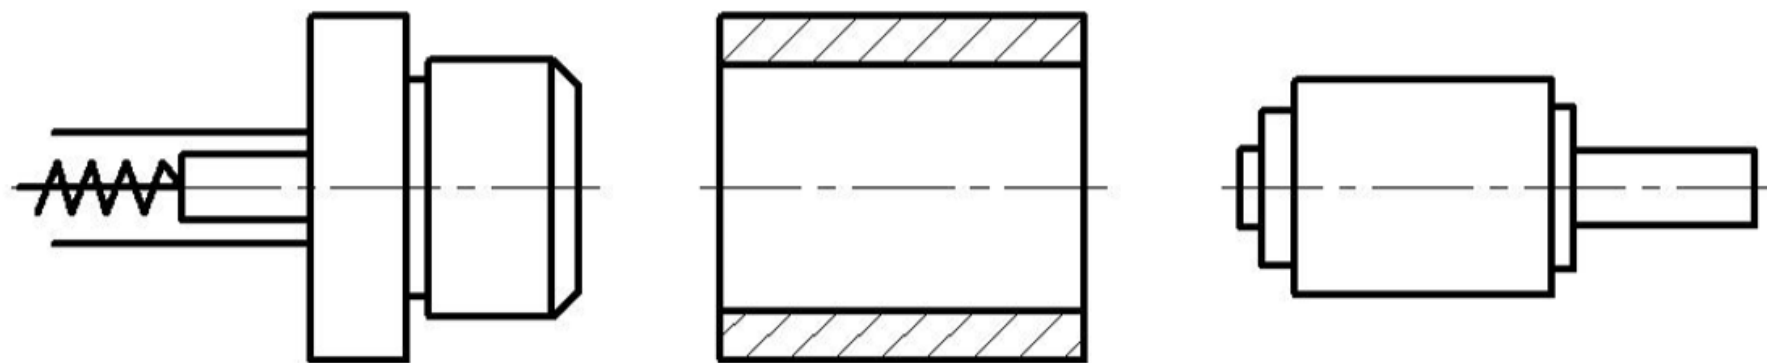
Прилади, які контактують по циліндричній поверхні
